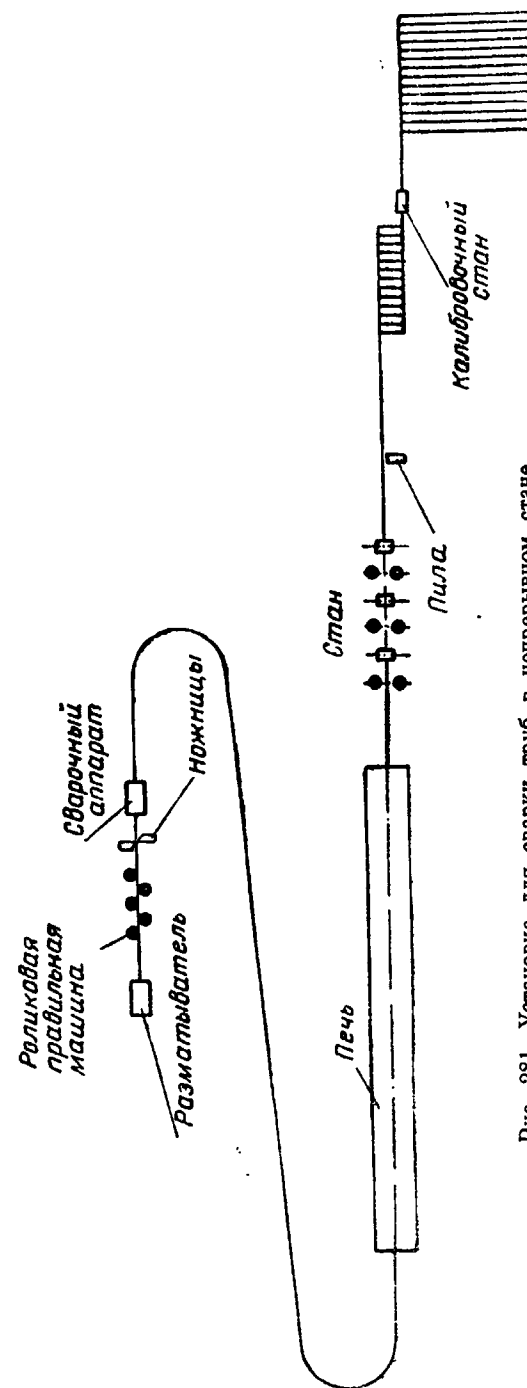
Установка для сварки труб в непрерывном стане
